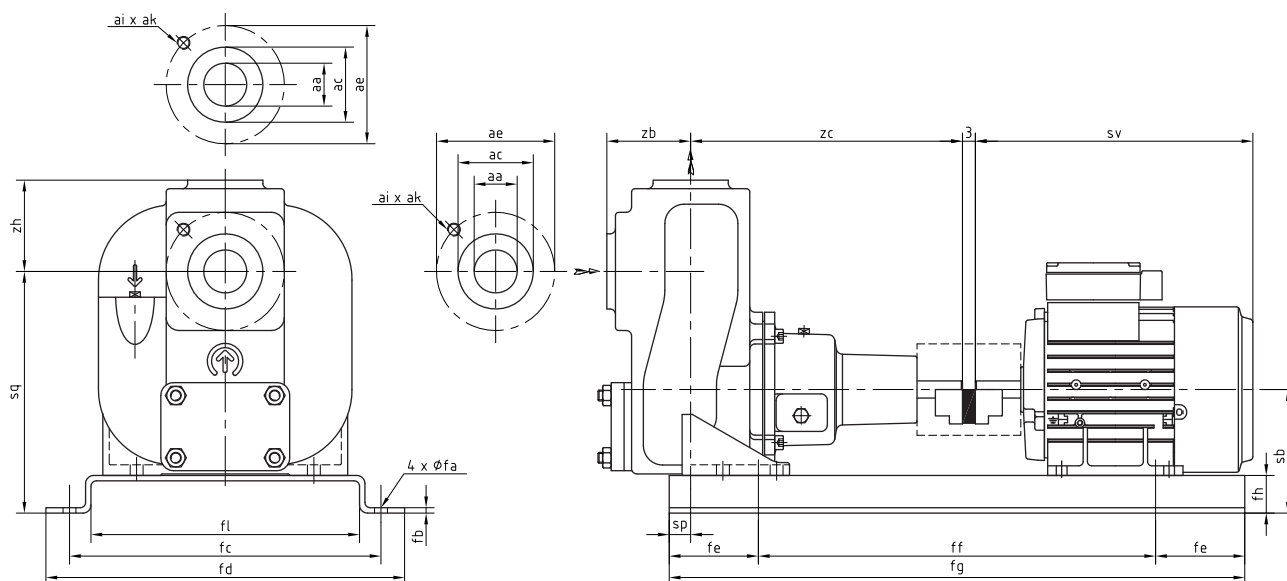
FRE - насосный агрегат А6 с соединениями по ISO 7005 PN20.
